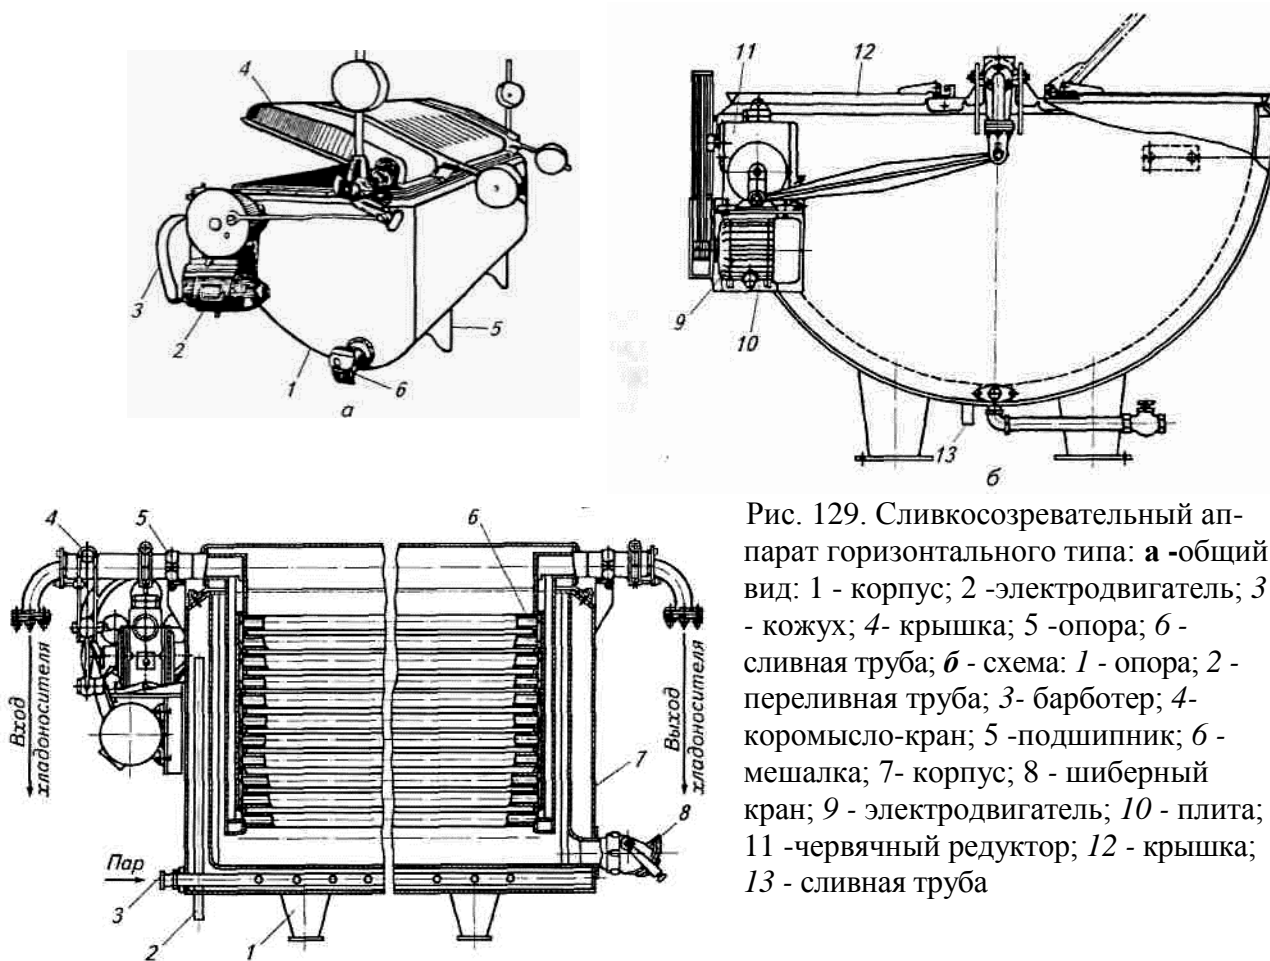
Сливкосозревательный аппарат горизонтального типа: а -общий вид: 1 - корпус; 2 -электродвигатель; 3 - кожух; 4- крышка; 5 -опора; 6 - сливная труба; б - схема: 1 - опора; 2 - переливная труба; 3- барботер; 4- коромысло-кран; 5 -подшипник; 6 - мешалка; 7- корпус; 8 - шиберный кран; 9 - электродвигатель; 10 - плита; 11 -червячный редуктор; 12 - крышка; 13 - сливная труба
